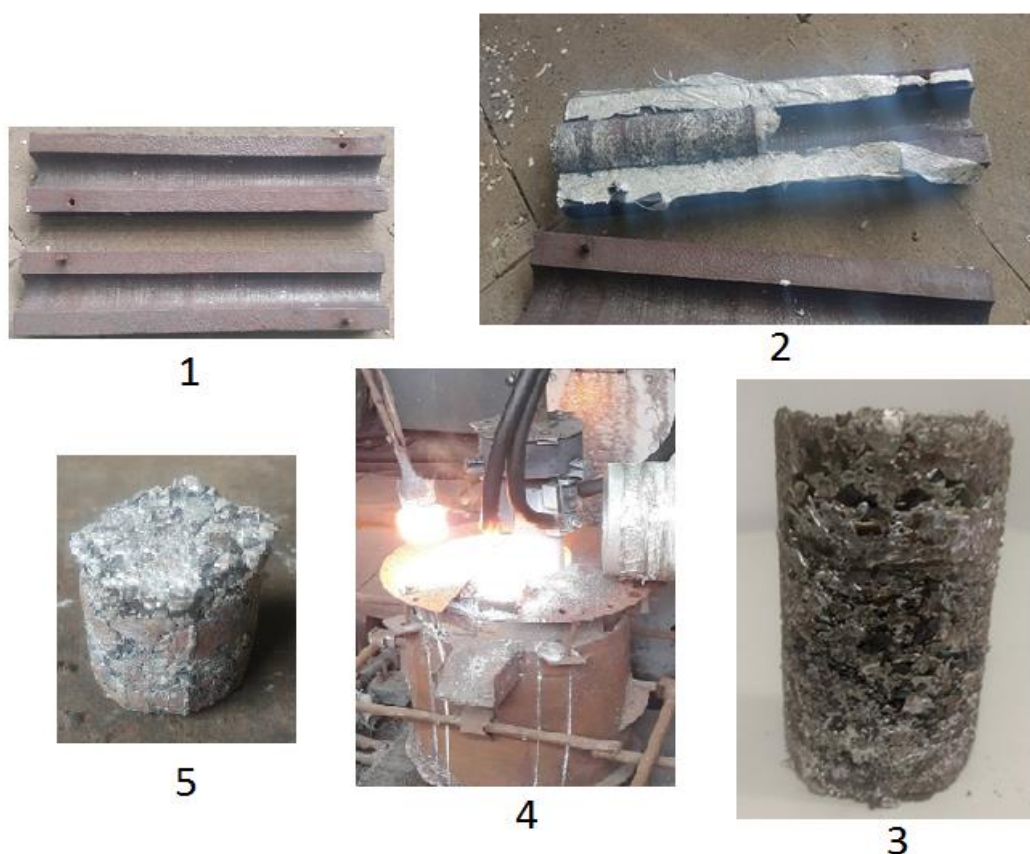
Эксперимент по изготовлению металлостружечного РЭ: 1 – кокиль; 2 – кокиль в разобранном виде с заготовкой металлостружечного РЭ; 3 – заготовка металлостружечного РЭ; 4 – процесс плавки; 5 – оплавленный остаток.
